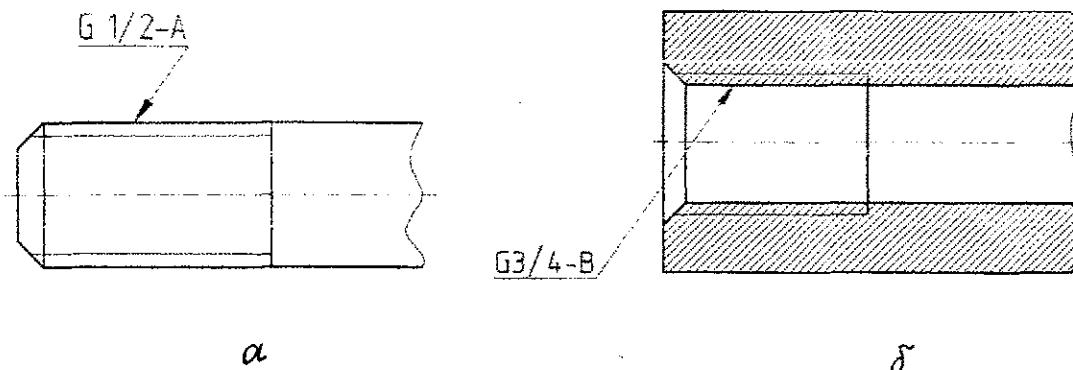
Пример обозначения трубной цилиндрической резьбы:
